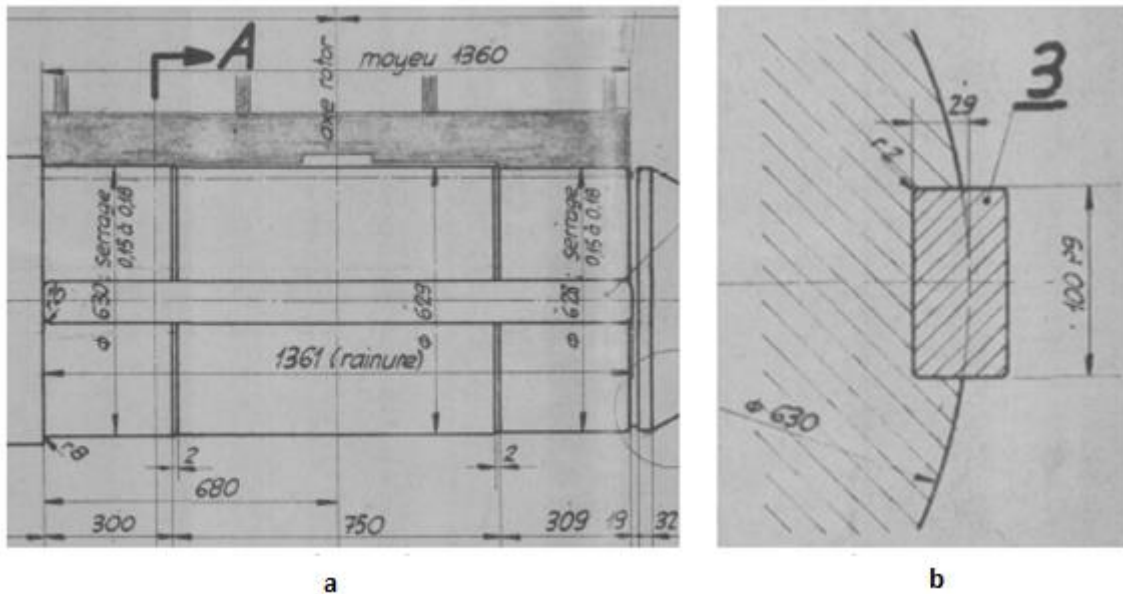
a) Desenho, em corte longitudinal, de veio, jante rotórica e chaveta; b) Desenho, em corte transversal, de pormenor da chaveta (adaptado de desenho técnico EDP).
